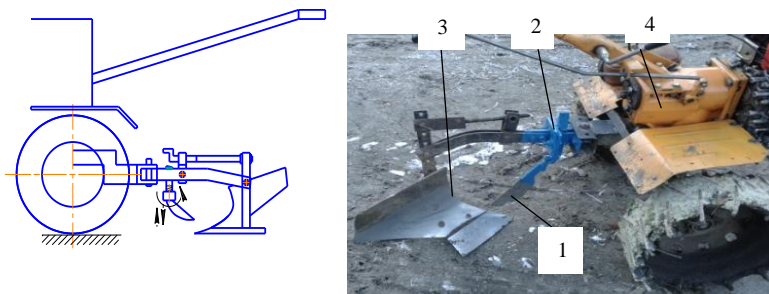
Схема і загальний вигляд модернізованого агрегату:
